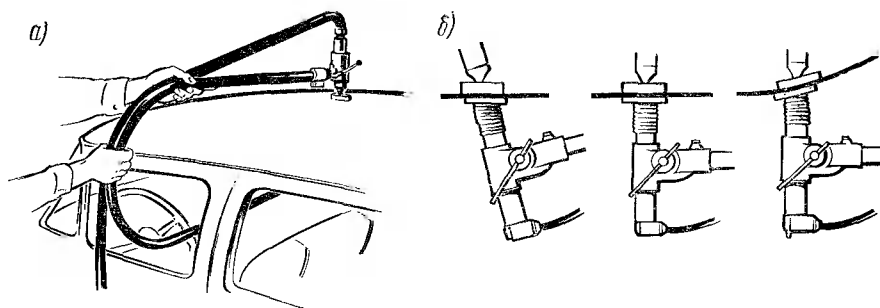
Разглаживание неровных поверхностей пневматическим устройством: а — работа молотком; б — самоустановка бойка молотка и поддержки на нужный угол
